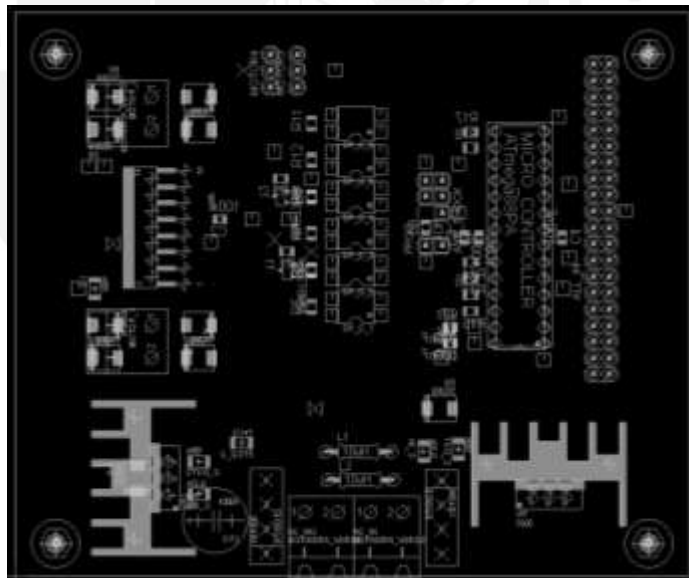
Cara de componentes: fuentes, controlador y motores.
